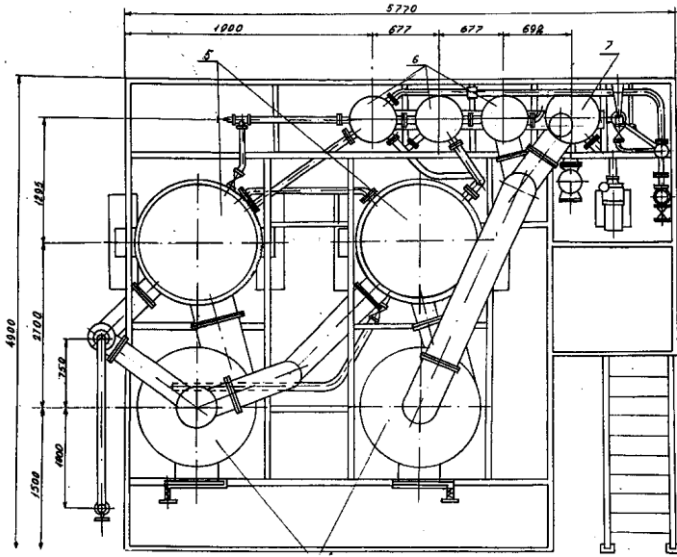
Двокорпусна вакуум-випарна установка циркуляційного типу: 1 - термокомпресор (інжектор); 2 - ежекторний блок; 3 - насос для згущеного молока; 4 - насос для конденсату; 5 - паронагрівачі (калоризатори); 6 - трубчасті підігрівачі; 7 - конденсатор; 8 - паровіддільники (сепаратори)
